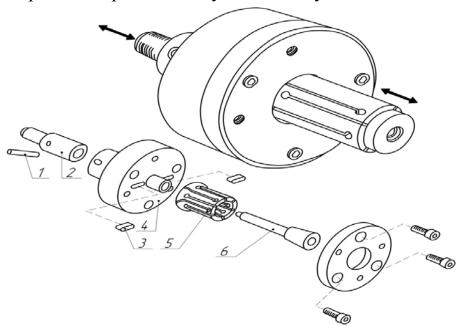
Шпиндельная разжимная фланцевая оправка с механизированным приводом: 1 — штифт; 2 — резьбовая втулка; 3 — шпонка; 4 — корпус; 5 — цанга; 6, 8 — винты; 7 — фланец
